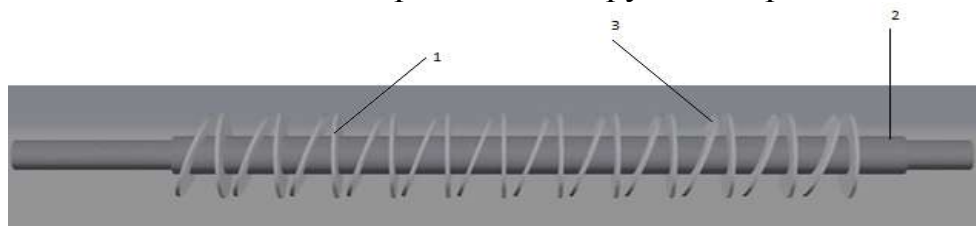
Ускоряющий направляющий цилиндрической формы
